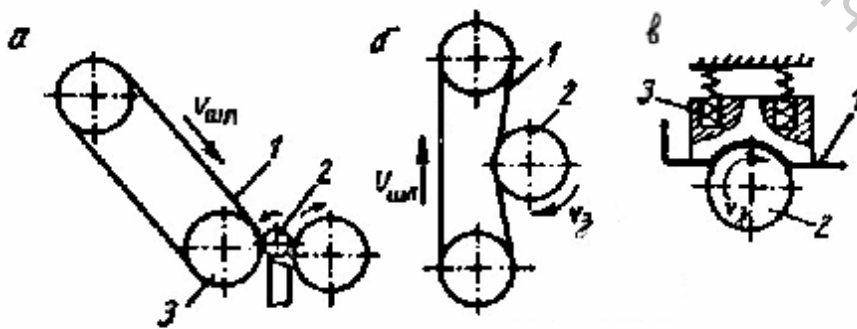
Схемы ленточного шлифования наружных поверхностей вращения: а- круглое бесцентровое; б- круглое наружное без копира и с копиром
